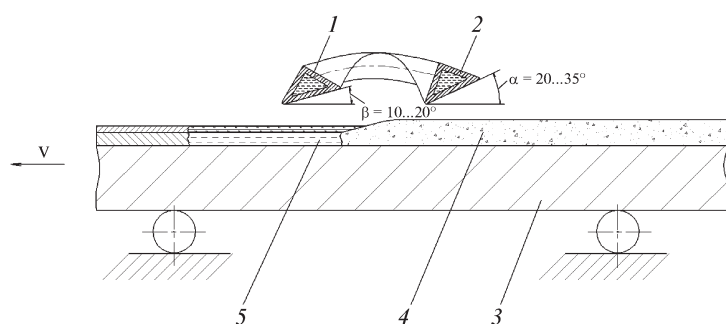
Индуктор для автоматической односторонней наплавки и схема осуществления 2-зонной наплавки ПОО и РО
